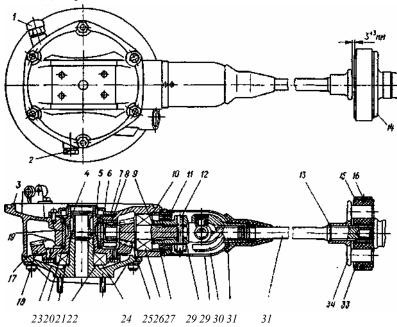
Главная передача мотоцикла "Днепр": 1 - шуп с сапуном; 2 - пробка сливного отверстия; 3 - картер; 4 - игольчатый ролик; 5 - ступица ведомой шестерни; 6 - крышка манжеты; 7 - карманная манжета; 8 - подшипник; 9, 22 - регулировочные прокладки; 10 - гайка подшипника; 11 - манжета; 12 - клиновой болт; 13 - стопорное кольцо; 14 - ведущая вилка упругой муфты; 15 - обойма упругой муфты; 16 - стопорное кольцо; 17 - картонная прокладка; 18 - ведомая шестерня; 19 - втулка картера; 20 - распорное кольцо; 21 - кольцо-сальник; 23 - крышка картер^» 24 - шариковый подшипник; 25 - ведущая шестерня; 26 - радиально-упорный шариковый подшипник; 27 - уплотняющее кольцо; 28 - вилка кардана; 29 - колпак кардана; 30; жесткий карданный шарнир; 31 - защитная муфта; 32 - карданный вал; 33 - упругая муфта; 34 - ведомая вилки упругой муфты
